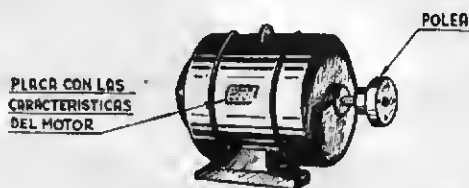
En el eje del motor está montada la polea que sirve para transmitir el movimiento a las máquinas accionadas por el mismo.
